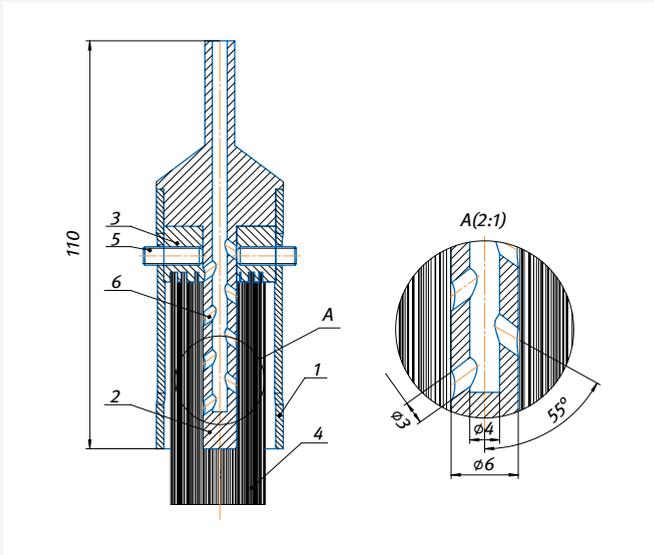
Гибкая абразивная щетка с внутренней подачей COTC
